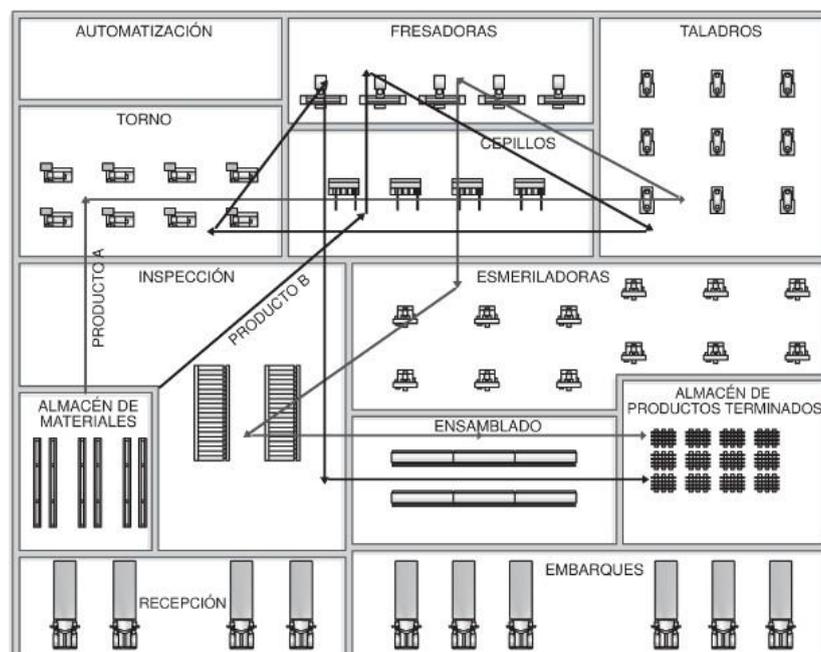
11 Ejemplo Distribución de planta Fuente: (García J. A., 2016)
